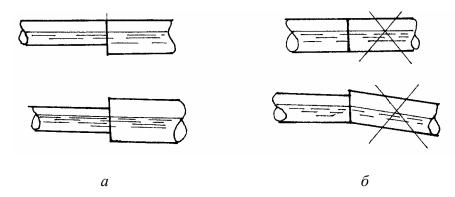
Схемы соединений трубопроводов: a — правильно; δ — неправильно
